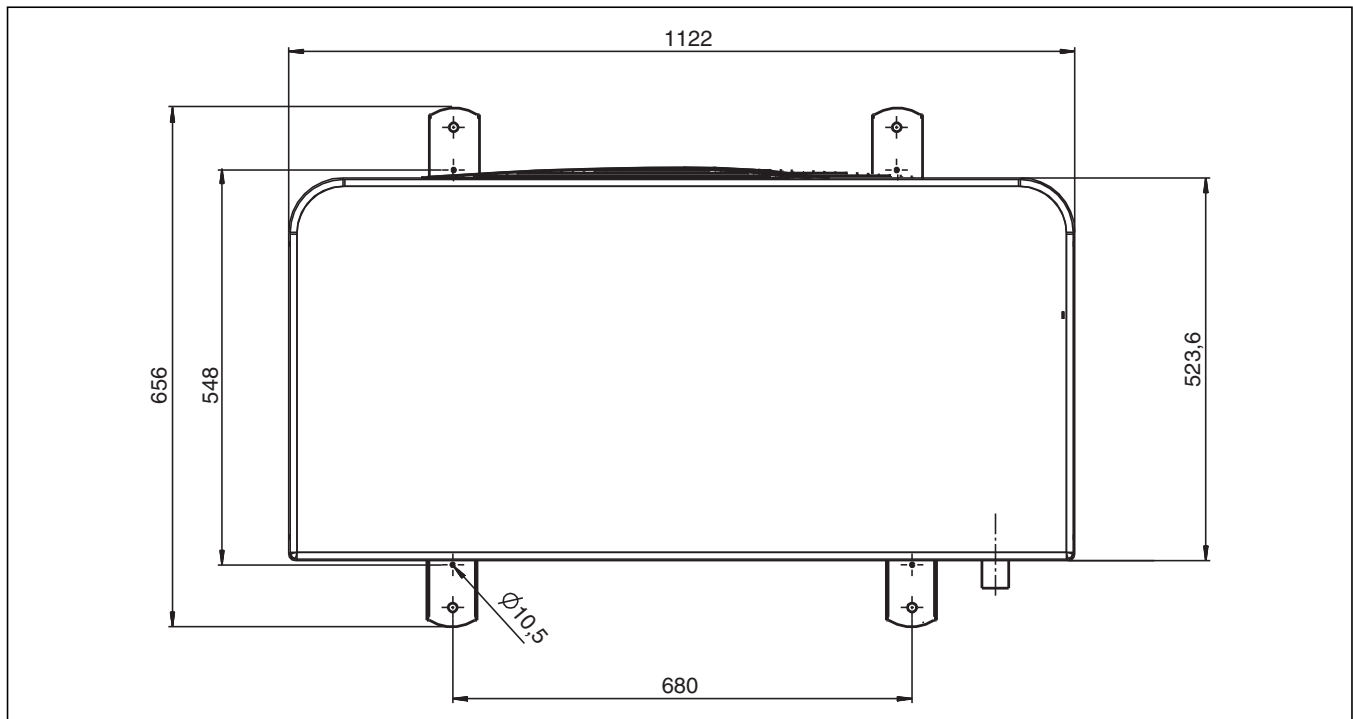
Размеры теплового насоса, верх, типоразмеры 13-17
